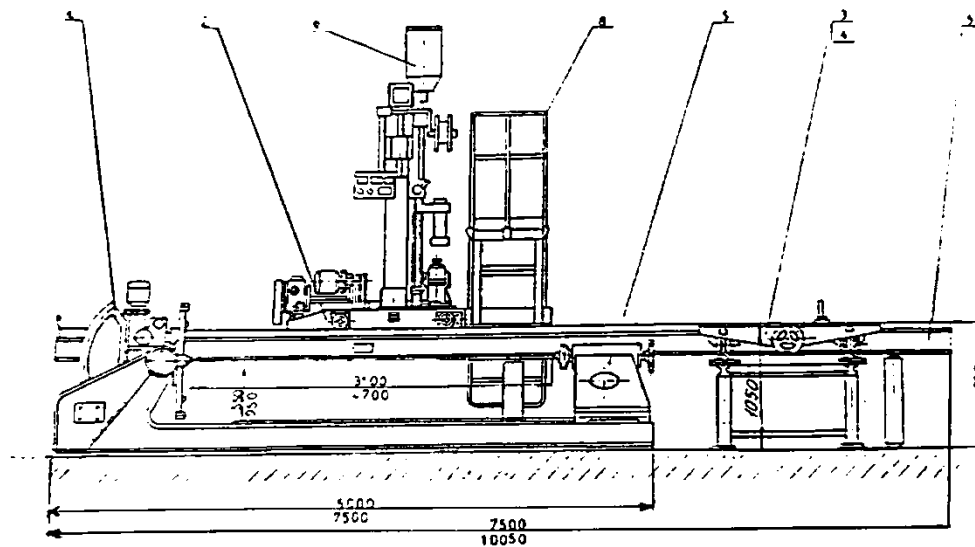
machine de rechargement par soudage (WELD CLAD)
